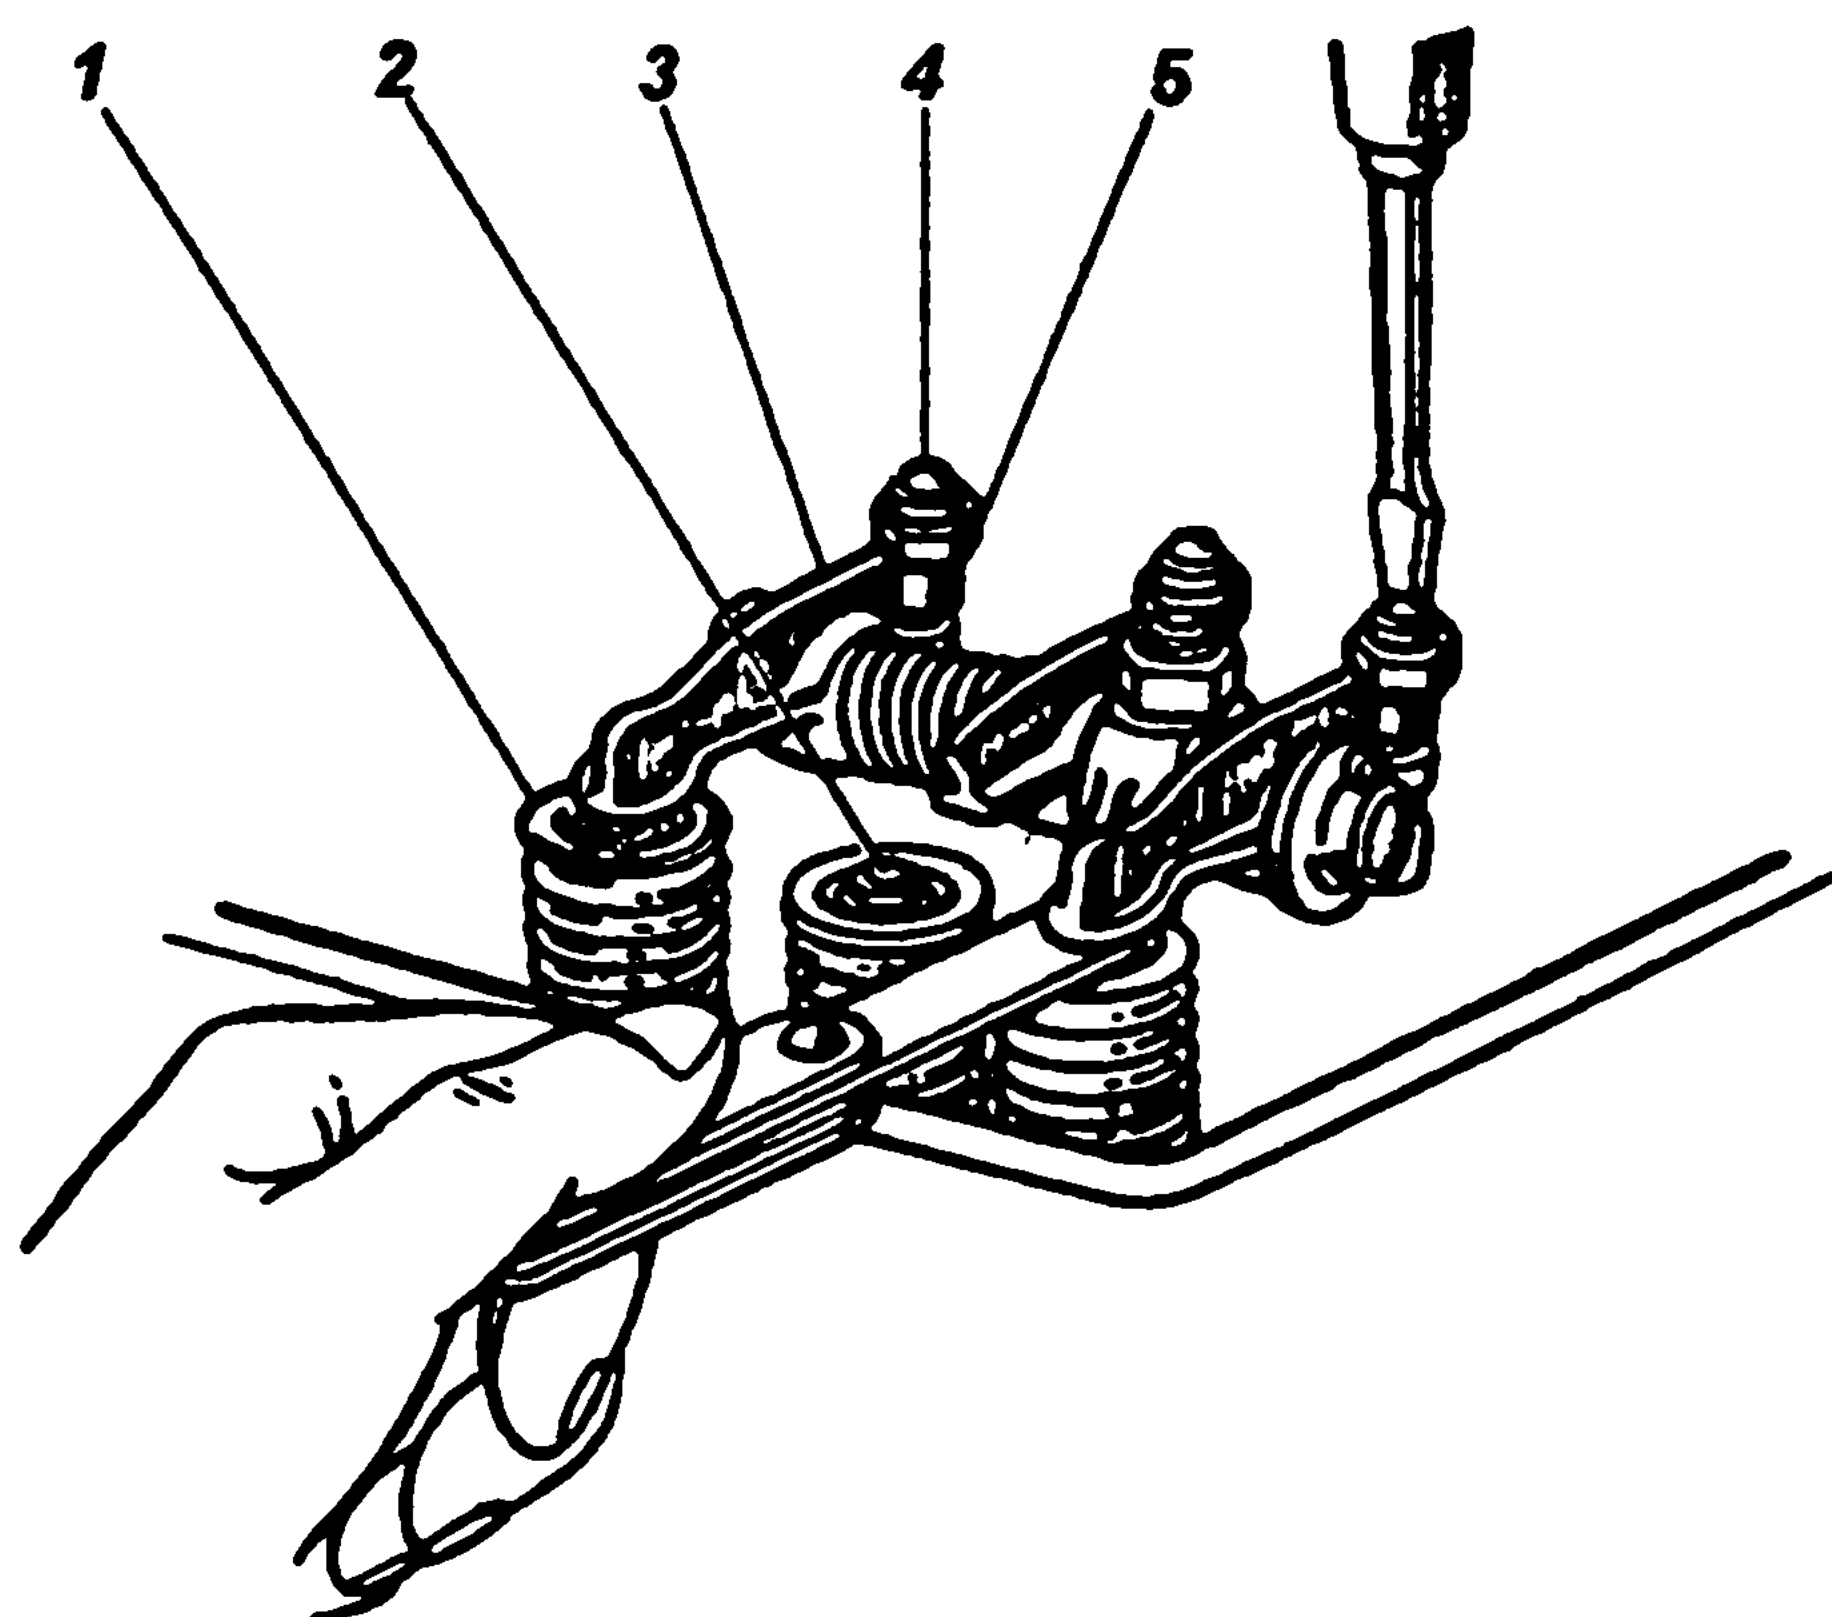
Регулировка зазора между коромыслом и клапаном:
